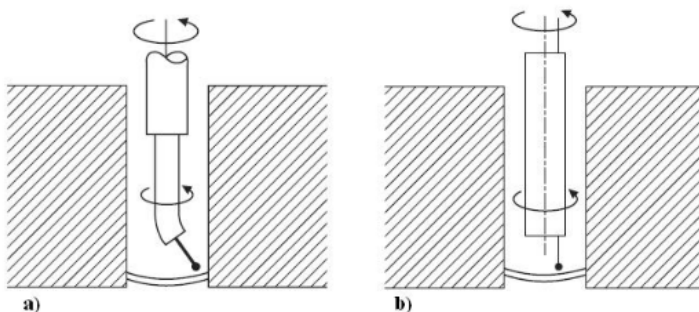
Soldagem em chanfro estreito com bico de contato rotativo: a) com furo inclinado; b) com furo excêntrico [6]
